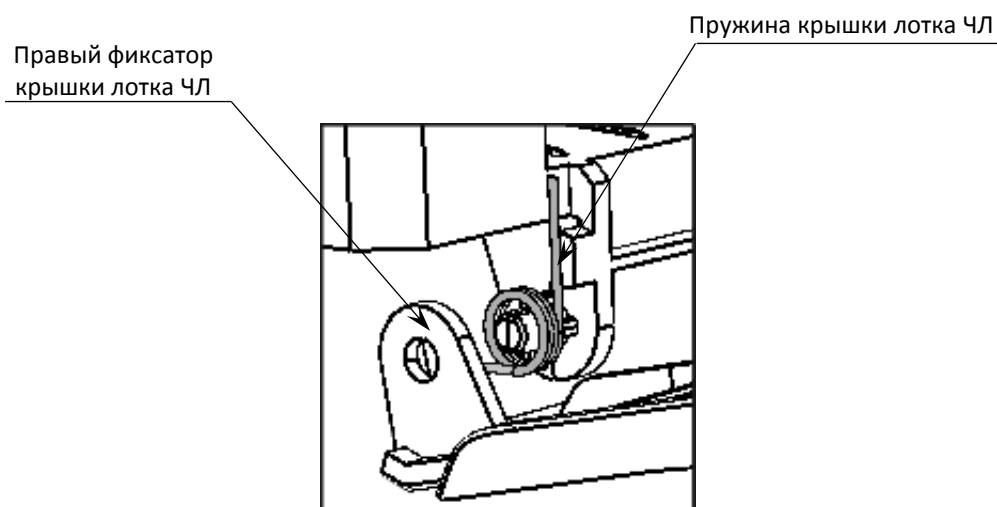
Отделение правого фиксатора крышки и пружина лотка ЧЛ
